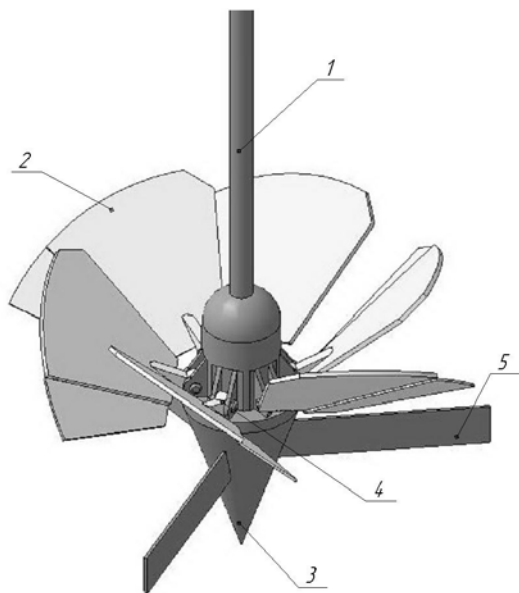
Запірний механізм: 1 – штанга; 2 – пелюстка; 3 – конус; 4 – шарнір; 5 – розпірка
